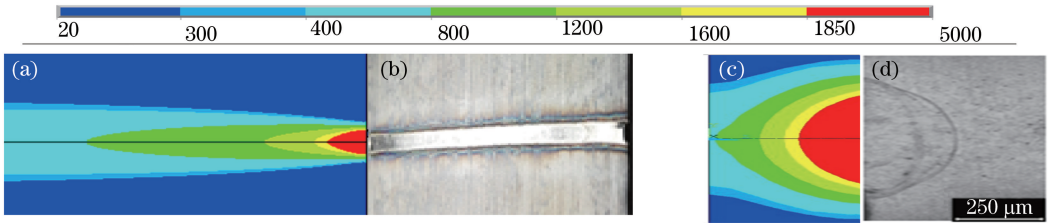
试验与模拟的焊缝形貌对比。(a) 模拟表面形貌; (b) 试验表面形貌; (c) 模拟截面形貌; (d) 试验截面形貌
